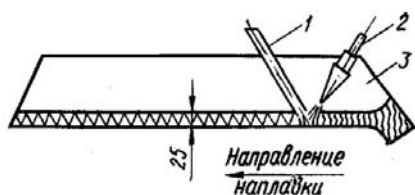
Схема наплавки лезвия лемеха твердым сплавом с помощью газовой горелки: 1 — пруток твердого металла; 2 — горелка; 3 — лемех
